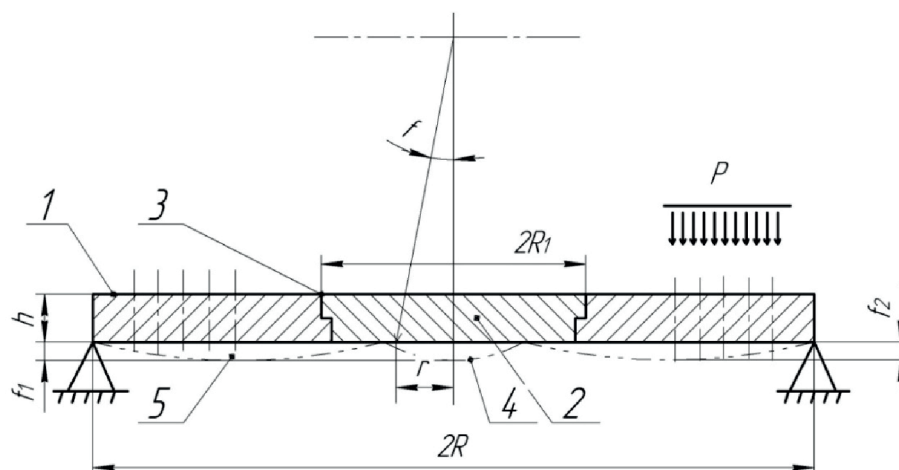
Схема деформаций корпуса составной матрицы с шарнирным закреплением по наружному контуру: 1 – большая часть корпуса матрицы; 2 – меньшая (центральная) часть корпуса матрицы; 3 – сквозной ступенчатый зазор; 4 – центр матрицы; 5 – формующие отверстия; φ – угол поворота к оси симметрии матрицы; r – текущее значение радиуса; R – радиус корпуса матрицы; R_1 – радиус центральной части корпуса матрицы; f_1 – величина прогиба центральной части матрицы; f_2 – величина прогиба большей (кольцевой) части матрицы; h – высота (толщина) корпуса матрицы; P – давление
